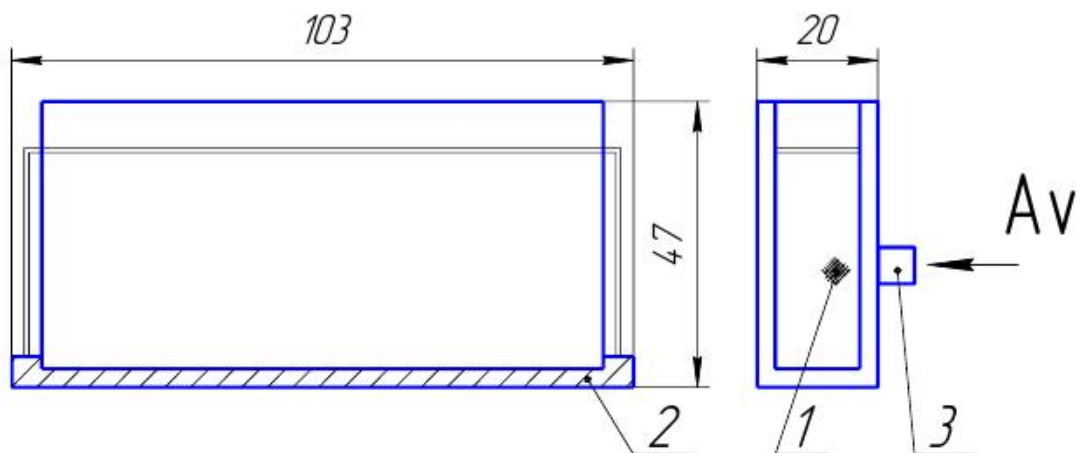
Приспособление для защиты корня шва при сварке встык швеллеров: 1 – сетка, 2 – корпус, 3 – насадок.
